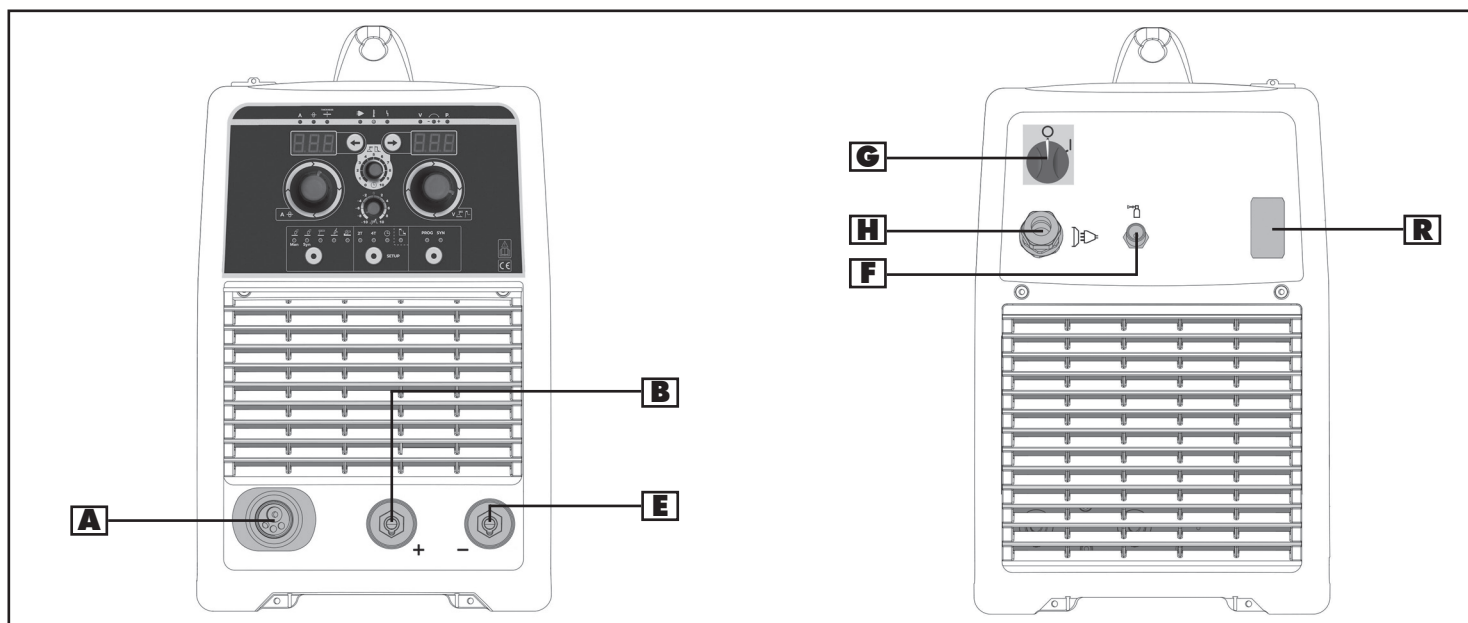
Vista delantera y trasera de la soldadora compacta
